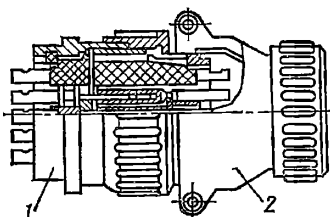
Цилиндрические приборные соединители типа ШР:
